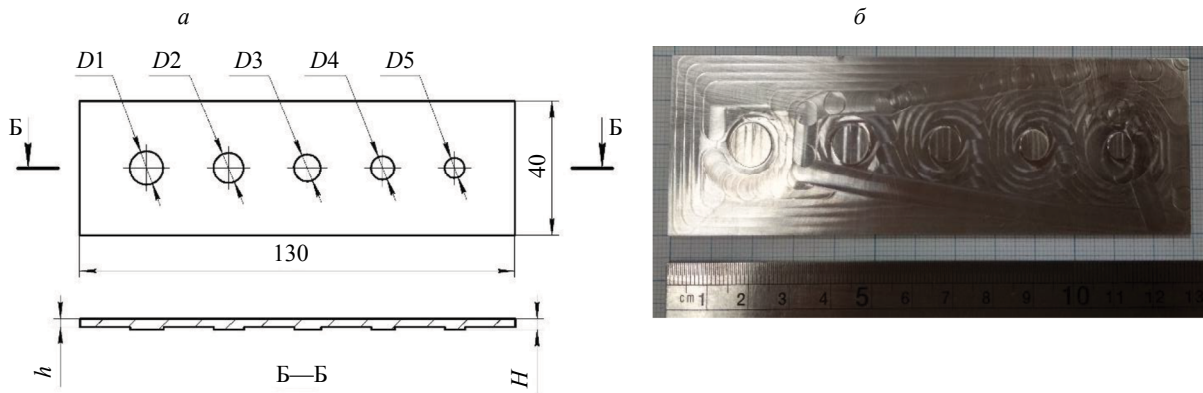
Образец настроечный с имитаторами сварных зон различного диаметра: эскиз (а); общий вид (б).
